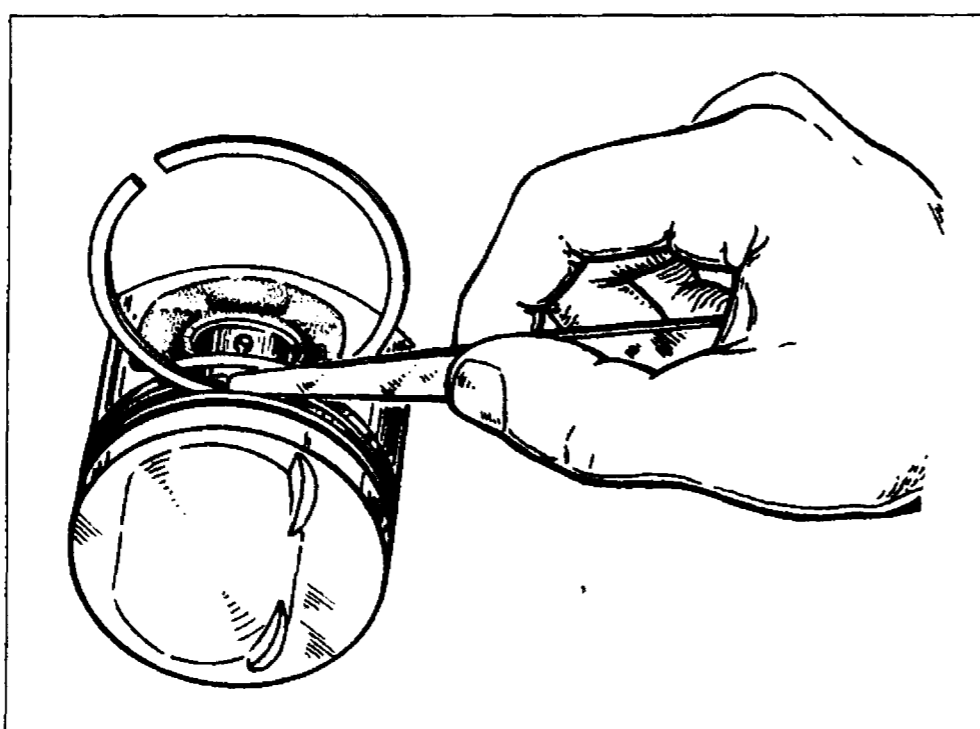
Проверка зазора между поршневыми кольцами и канавками
